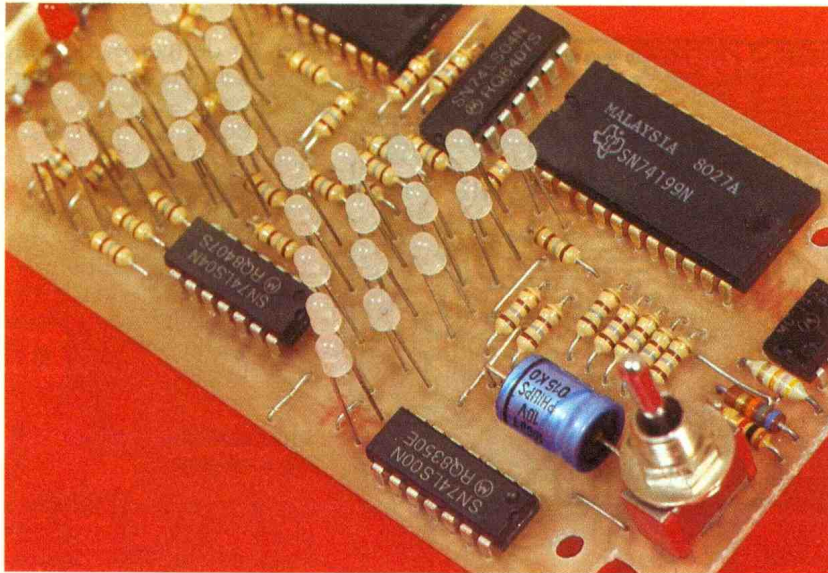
Les DEL doivent toutes avoir la même hauteur pour arriver sur la face avant du boîtier.
